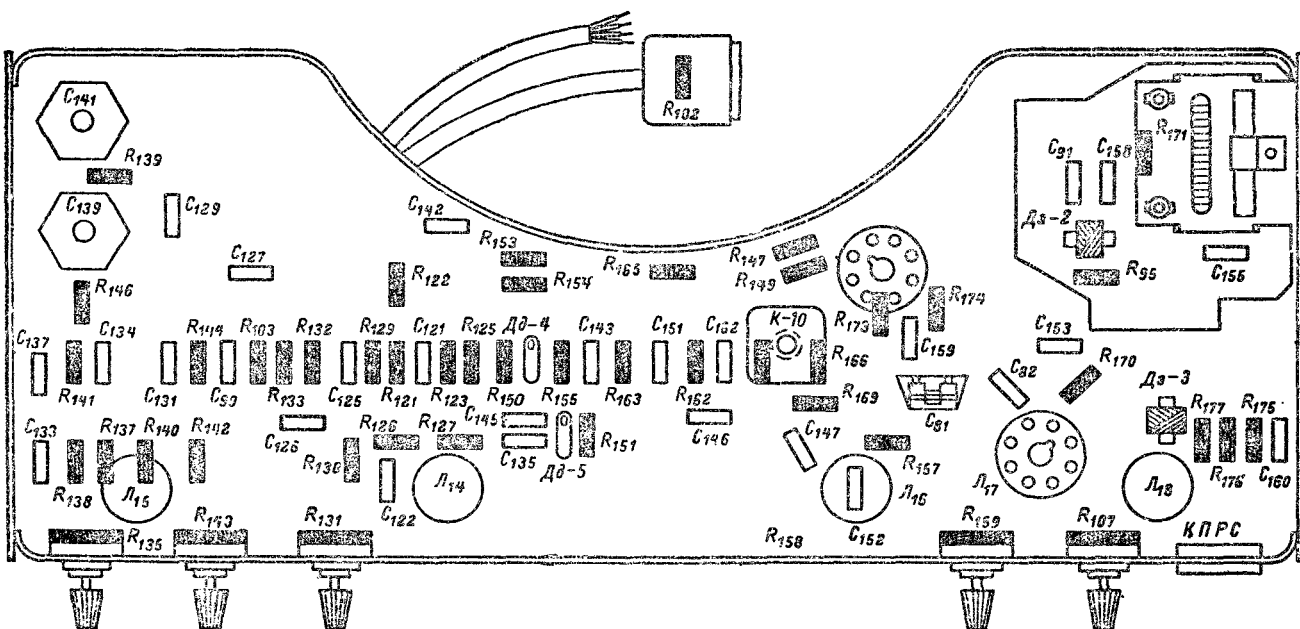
Расположение деталей на шасси блока развертки телевизора «Радий-Б» (вид со стороны монтажа).
